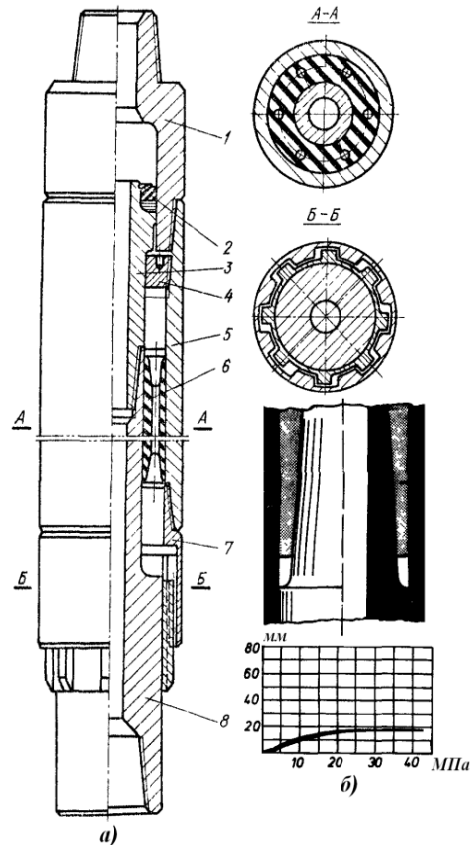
Амортизатор Shock-Sub фірми Drilko Oil Tools
